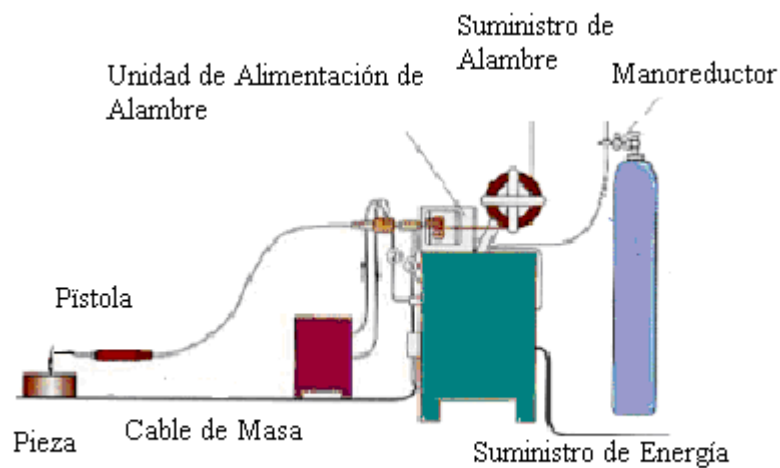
Elementos de la soldadura por arco en atmósfera inerte y con electrodo consumible
